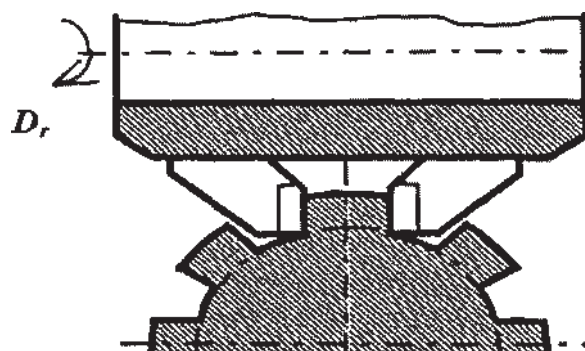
Схема фрезерования боковых поверхностей шлицев специальной торцевой фрезой
